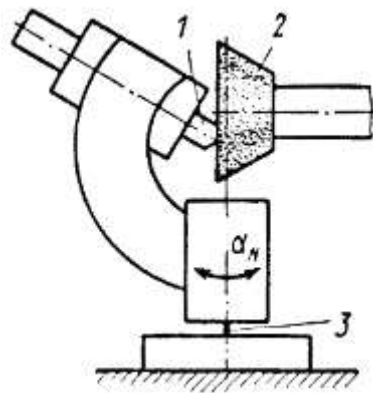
Схема двухплоскостной заточки сверла:
